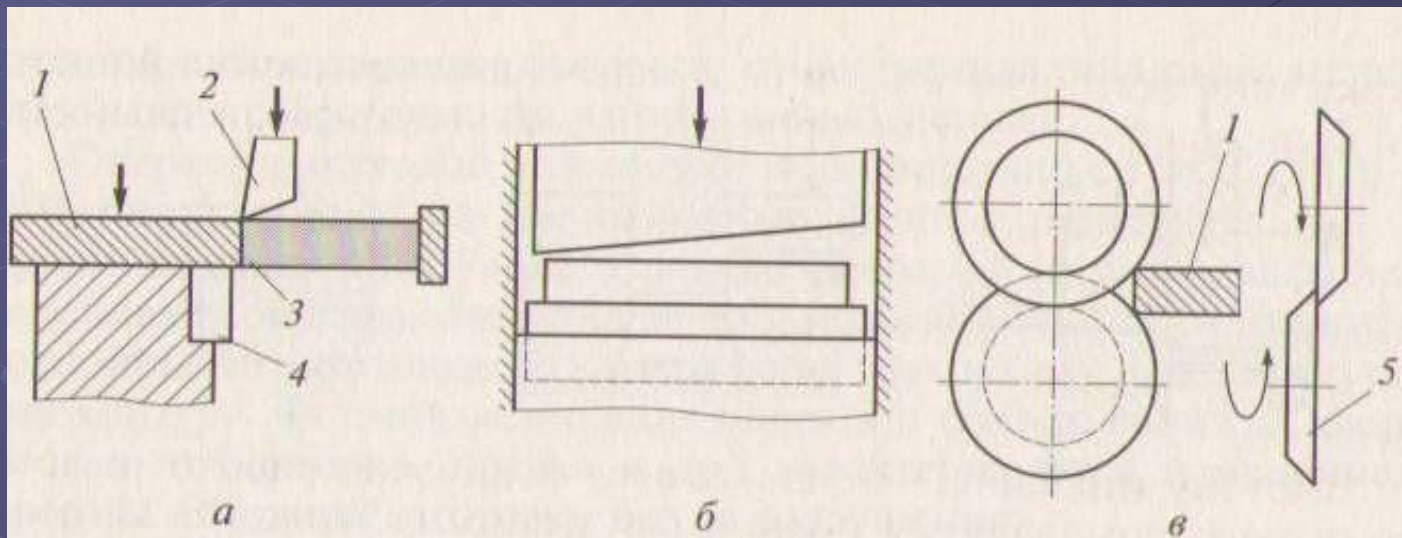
Схемы резки на ножницах: а – гильотинных с параллельными ножами; б – то же, с наклонными ножами; в – дисковых; 1 – исходный материал; 2 – подвижный нож; 3 – заготовка (деталь); 4 – неподвижный нож; 5 – дисковый нож; \rightarrow – направленное действие режущего усилия; \curvearrowright – направления вращения дисковых ножей
